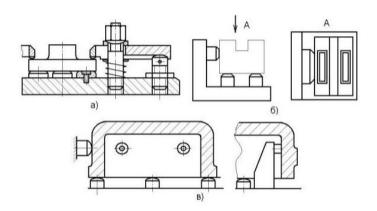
Схемы установки заготовок плоскими поверхностями на: а – опорные шайбы; б – опорные пластины; в – точечные опоры.
